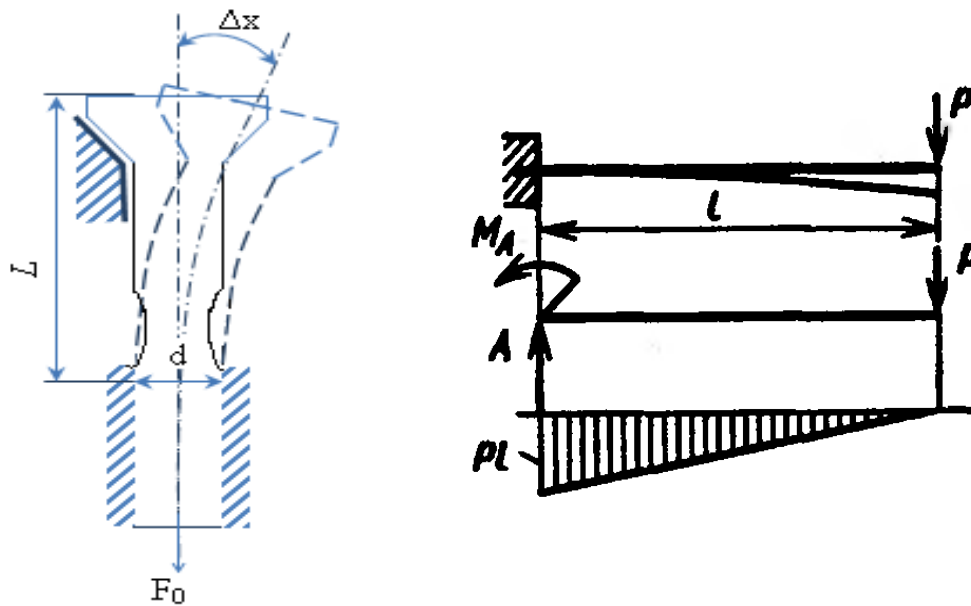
Схема дії навантажень пластини гвинтом в корпус фрези
